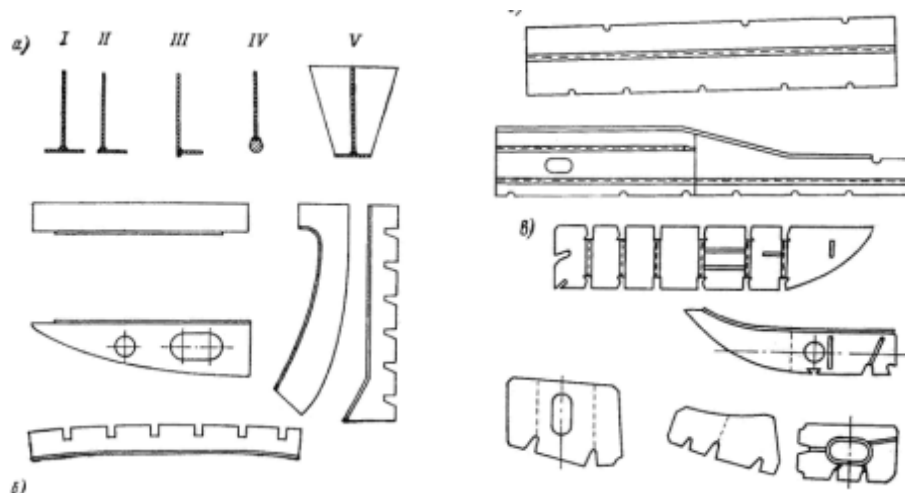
Вузли корпусних конструкцій: а – таврові балки; б – днищові стрінгери; в – флори
